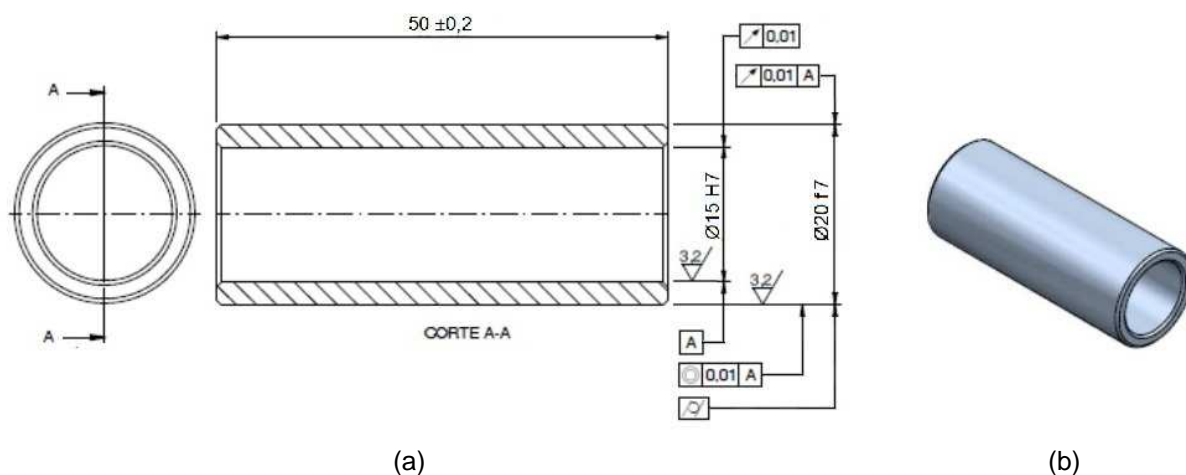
Dimensões do contra-corpo de aço inoxidável AISI 304: (a) Detalhes de fabricação (b) Vista em perspectiva.
